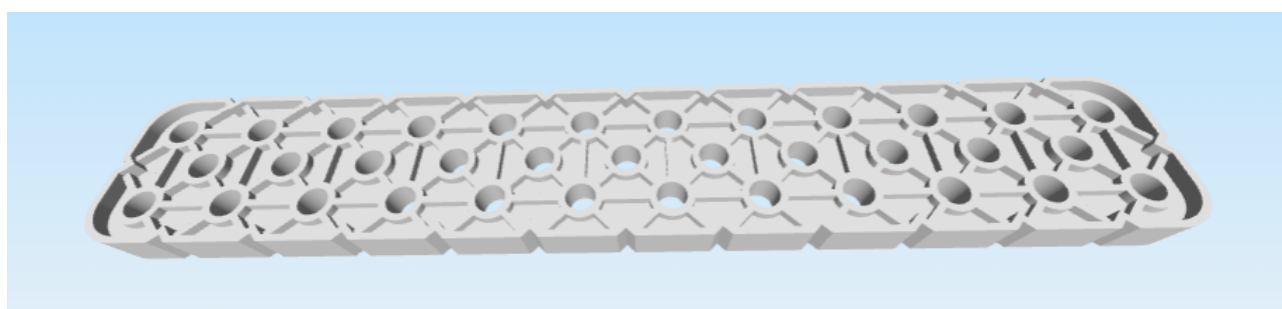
Díl 2x8 Smooth Panel (228-2500-524) VEX – horní strana
